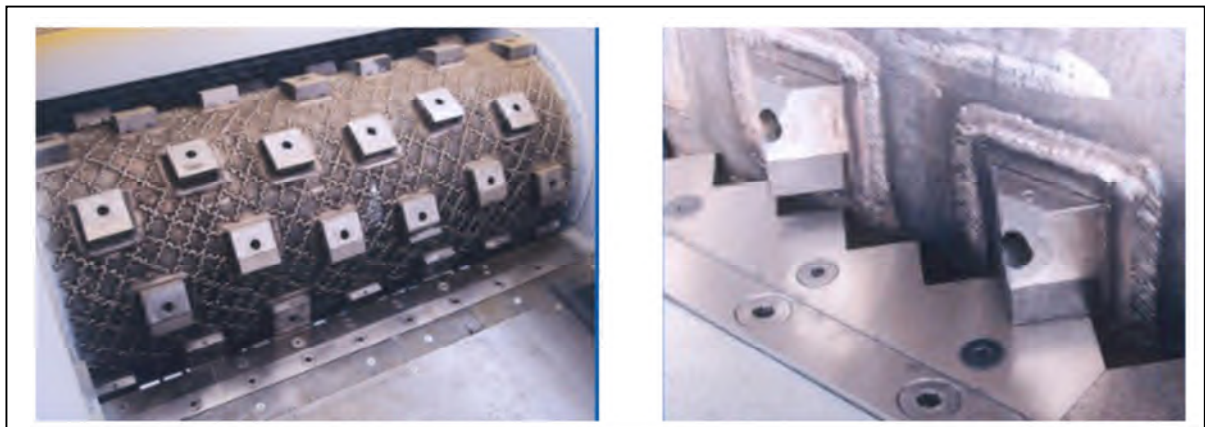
Déchiqueteur mono rotor à grille de calibrage
